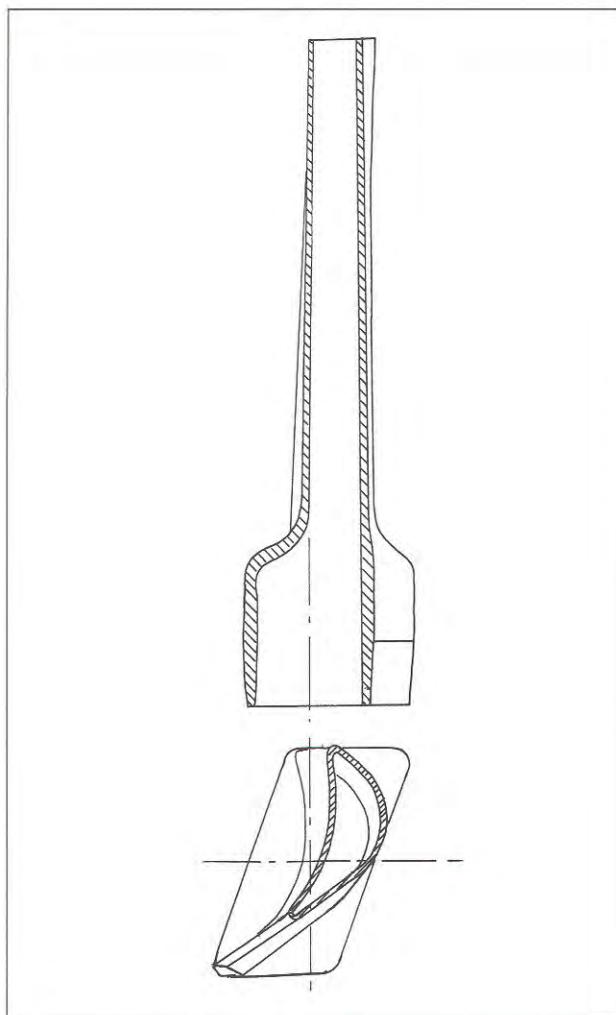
Чертеж полой лопатки турбины турбореактивного двигателя Юнкерс 109-004 В-1
